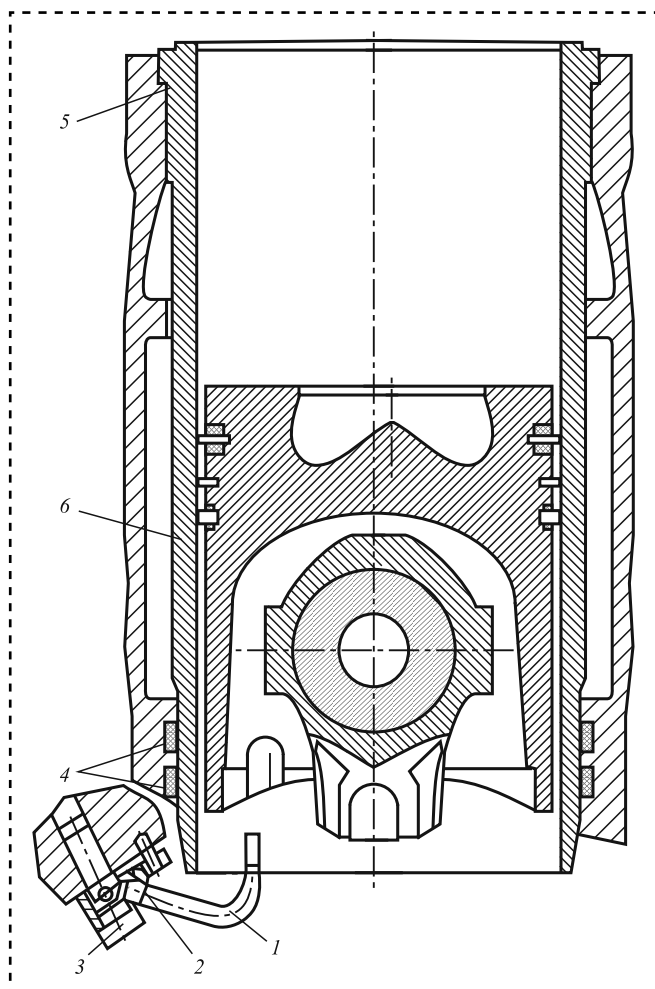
Схема установки гильзы и форсунки охлаждения в корпусе блока цилиндра:
